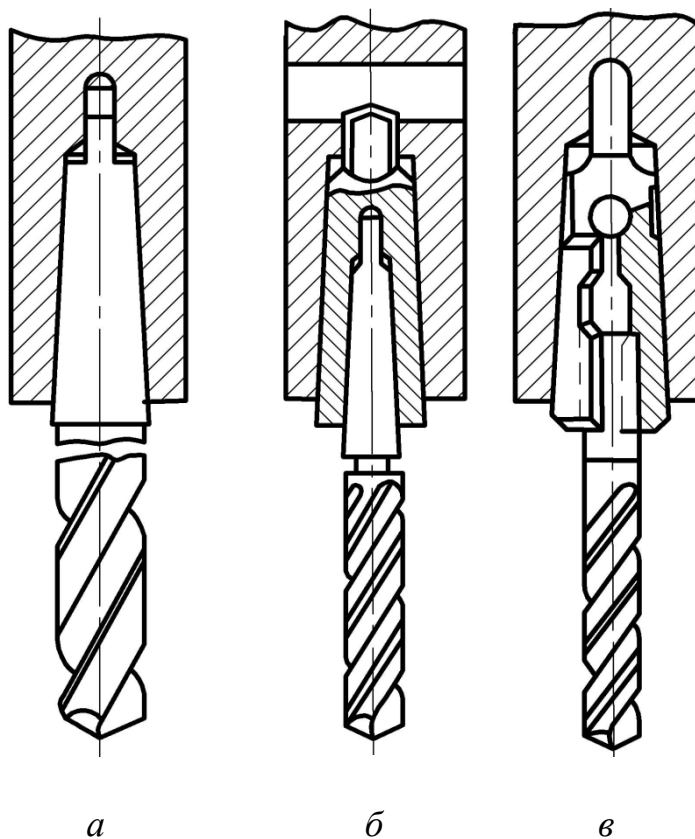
Инструменты и втулки, устанавливаемые в шпиндели станков
